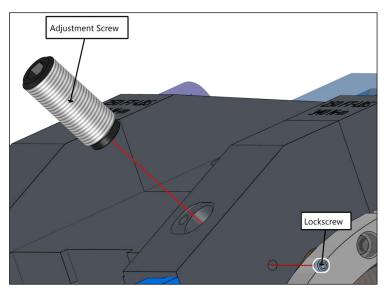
TORNILLO DE AJUSTE (IZQUIERDA) Y TORNILLO DE BLOQUEO (DERECHA)
